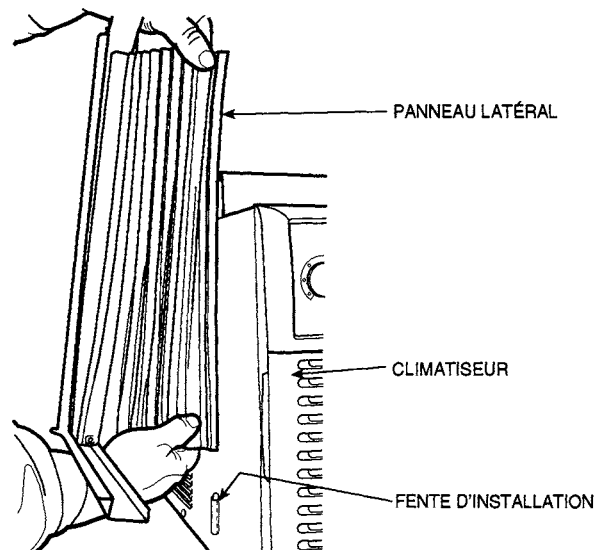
INSTALLATION DE LA PIÈCE CENTRALE DU PANNEAU LATÉRAL
